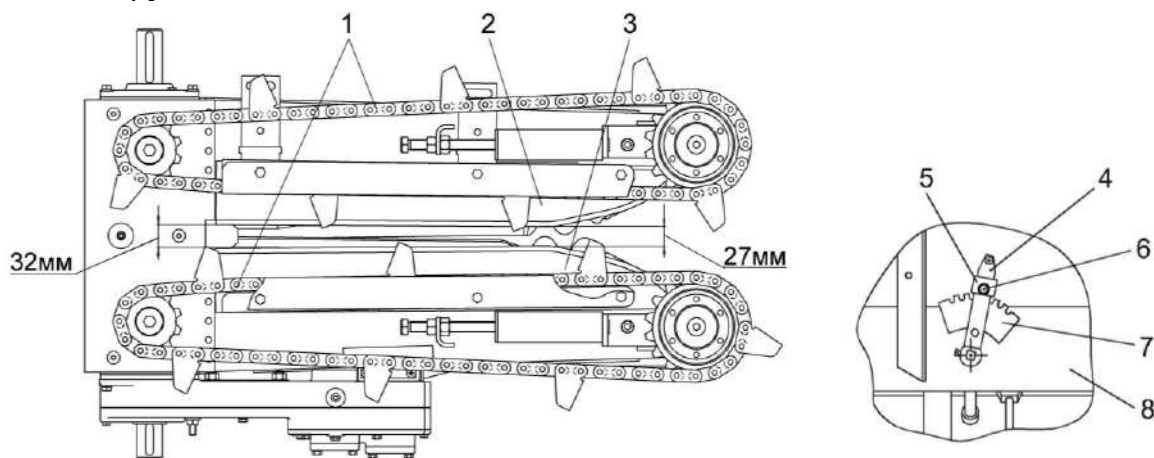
Регулировка лабиринтного уплотнения
